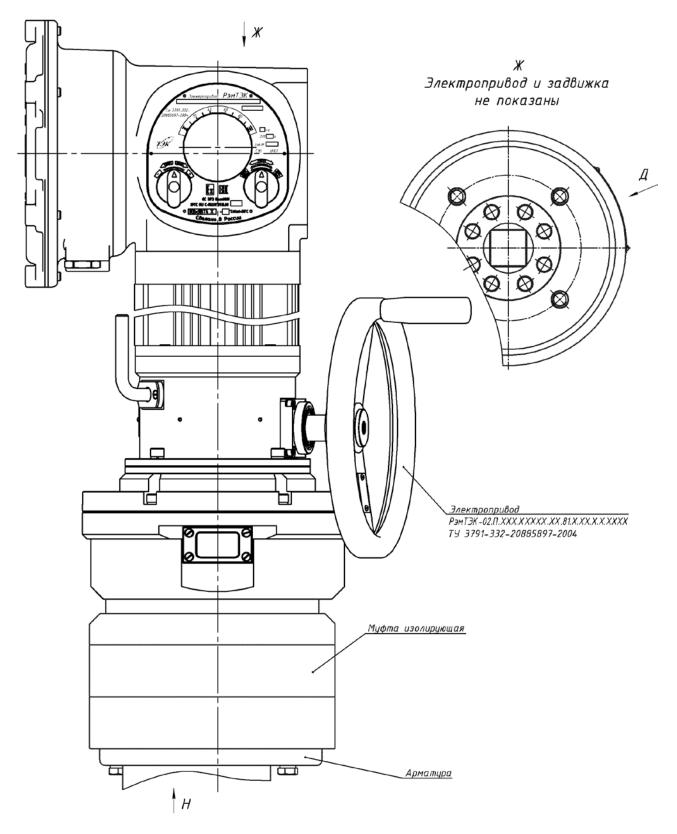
Чертеж средств взрывозащиты РэмТЭК-02 неполнооборотного исполнения конструктивного исполнения "81" в сборе с муфтой изолирующей
